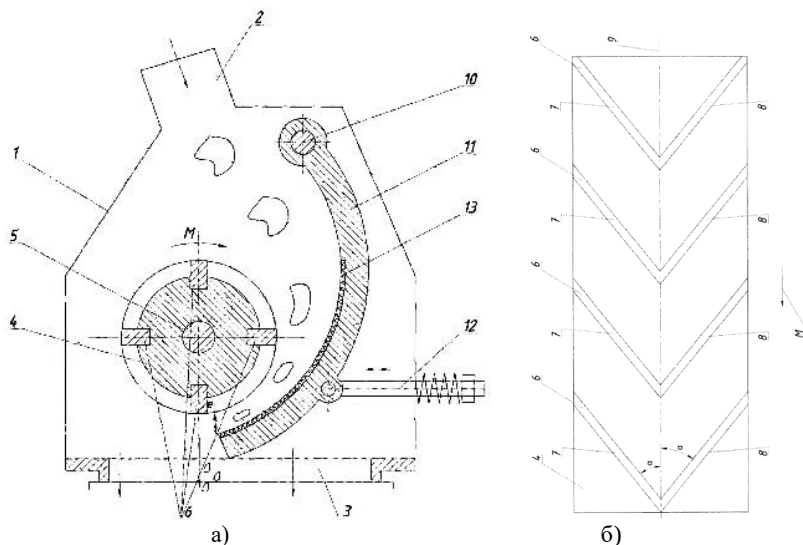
а) Роторная дробилка; б) развертка ротора с билами
